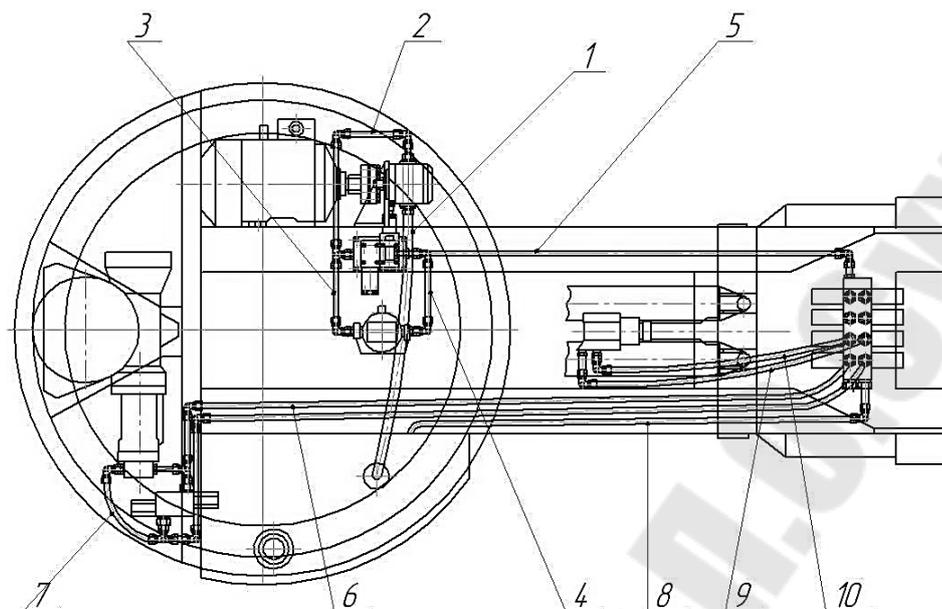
Монтажная схема трубопроводов на подъемнике
